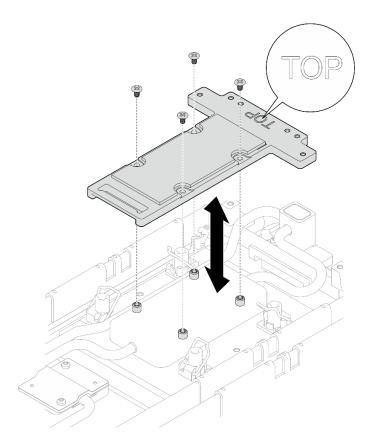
Entfernen der Kühlplatte für das mittlere Laufwerk
